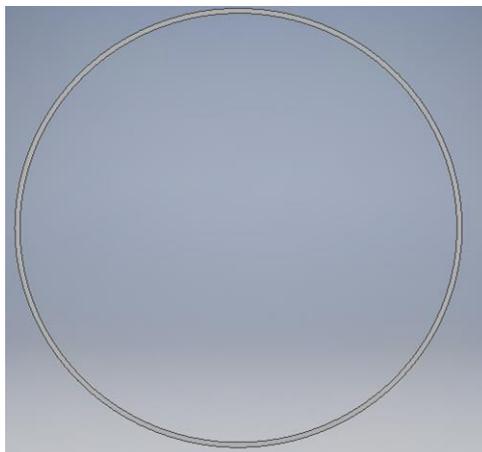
Профильный вид CAD - модели защитного кожуха.
